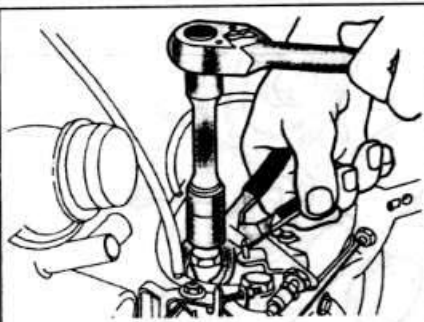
Отвертывание заглушки верхней части корпуса ТНВД на автомобилях выпуска с 1988 г.
